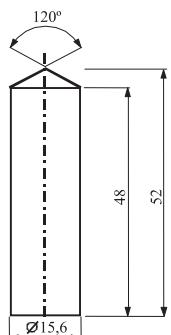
Цилиндрический бронзовый поршень; размеры в мм
